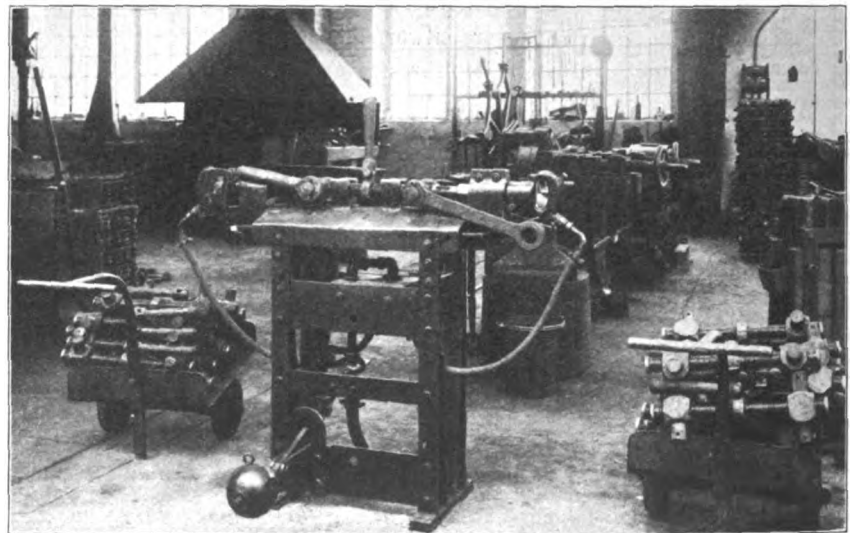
Maschine zum Warmaufrichten des Muttergewindes.
